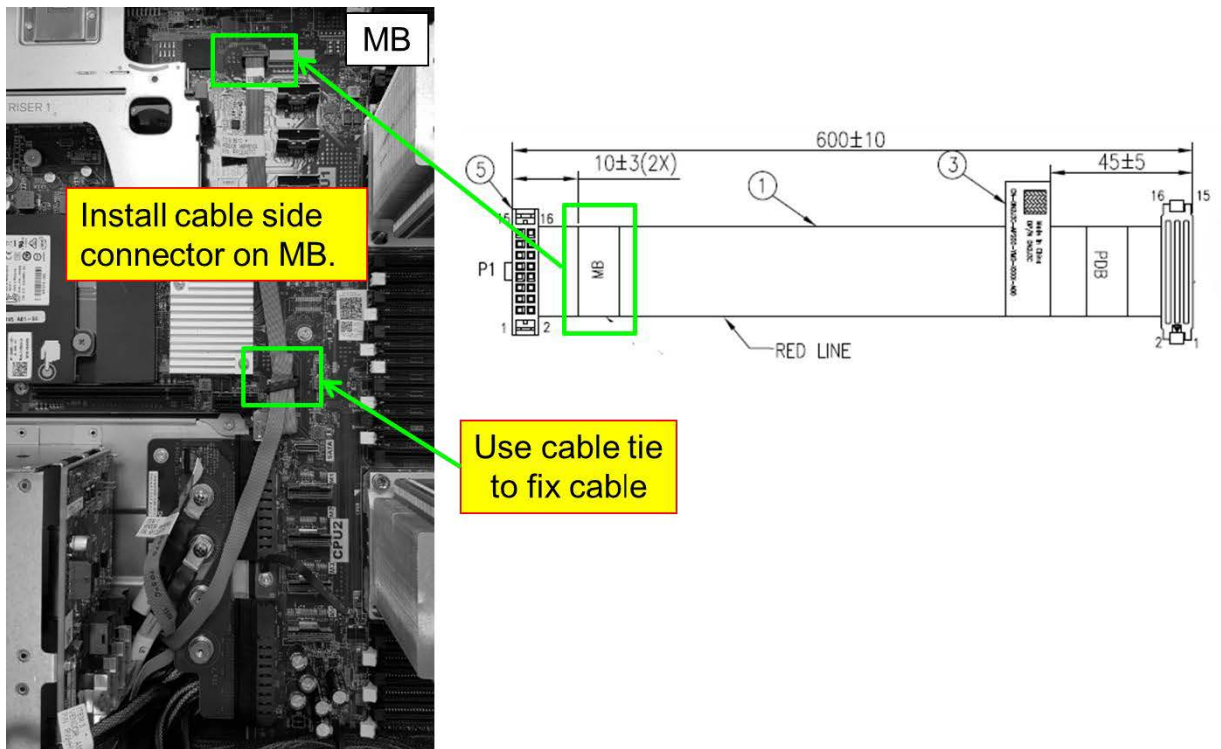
Assemblage du câble IDC (MB-PDB) vers MB
